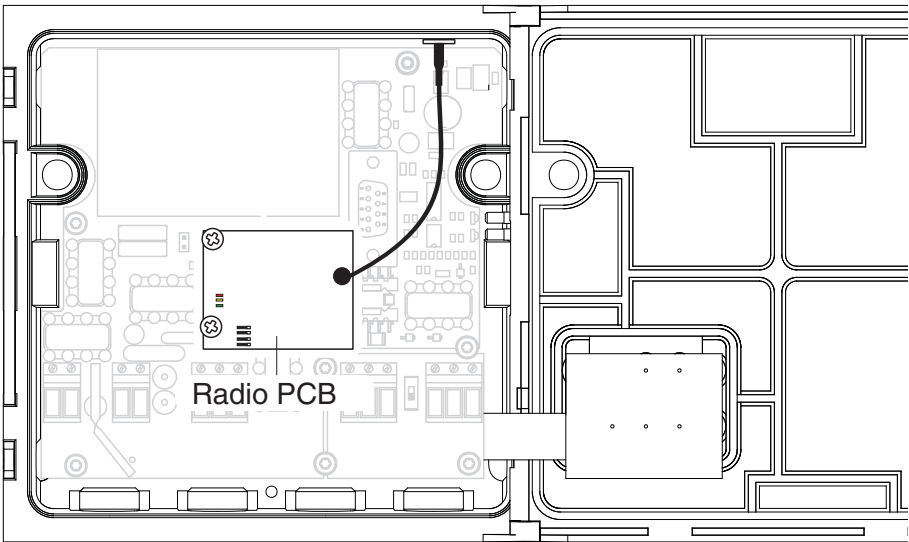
Módulo MIQ/WL PS com rádio PCB
